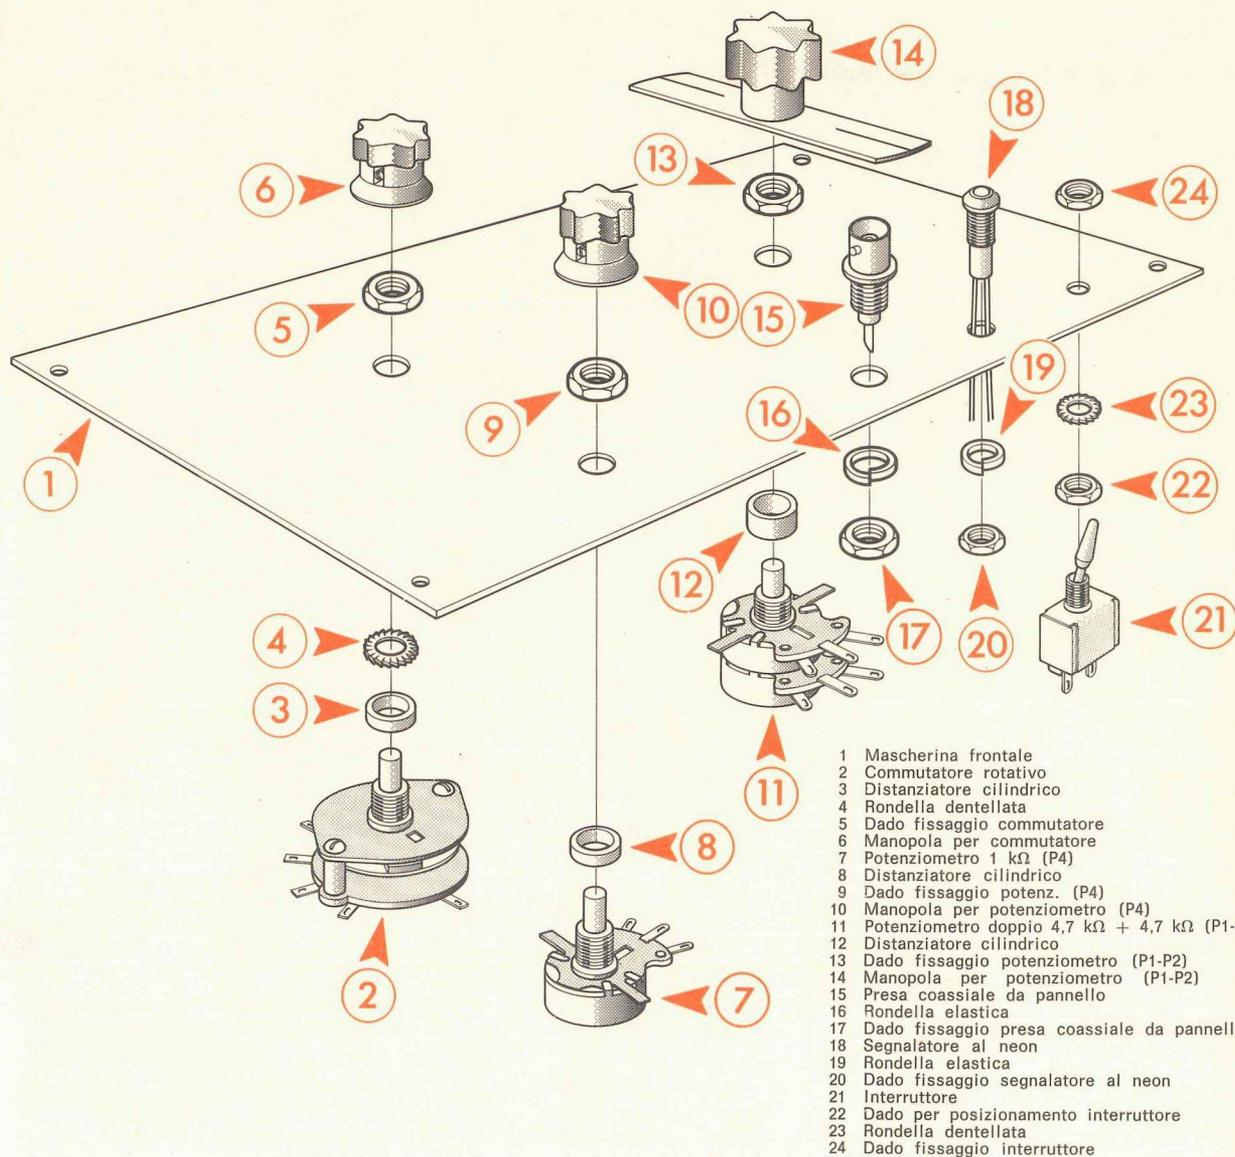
Esploso di montaggio dei componenti sulla mascherina frontale.
